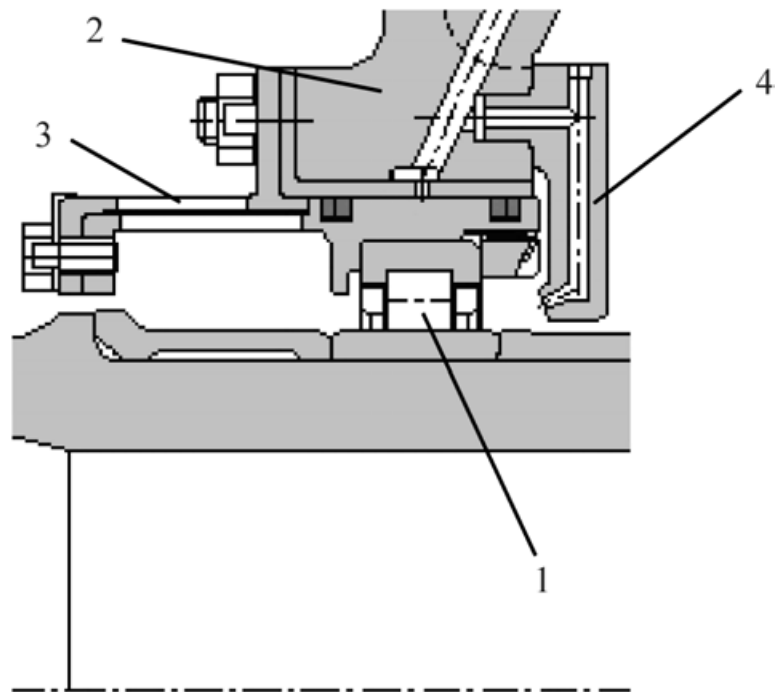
Проміжна опора ротора НД з роликопідшипником
